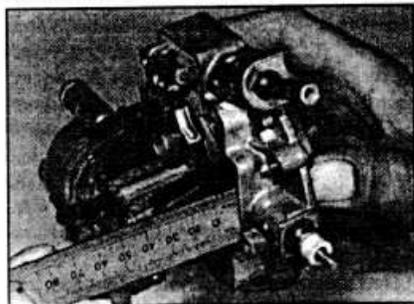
А.26. Проверка регулировки уровня поплавка карбюратора TLD.
